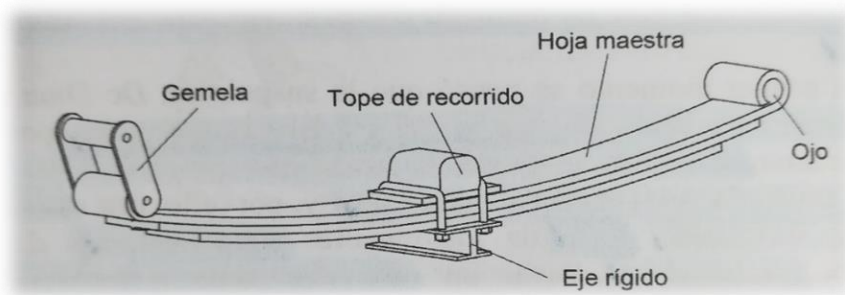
Elementos de la ballesta. Fuente: Ingeniería del automóvil
